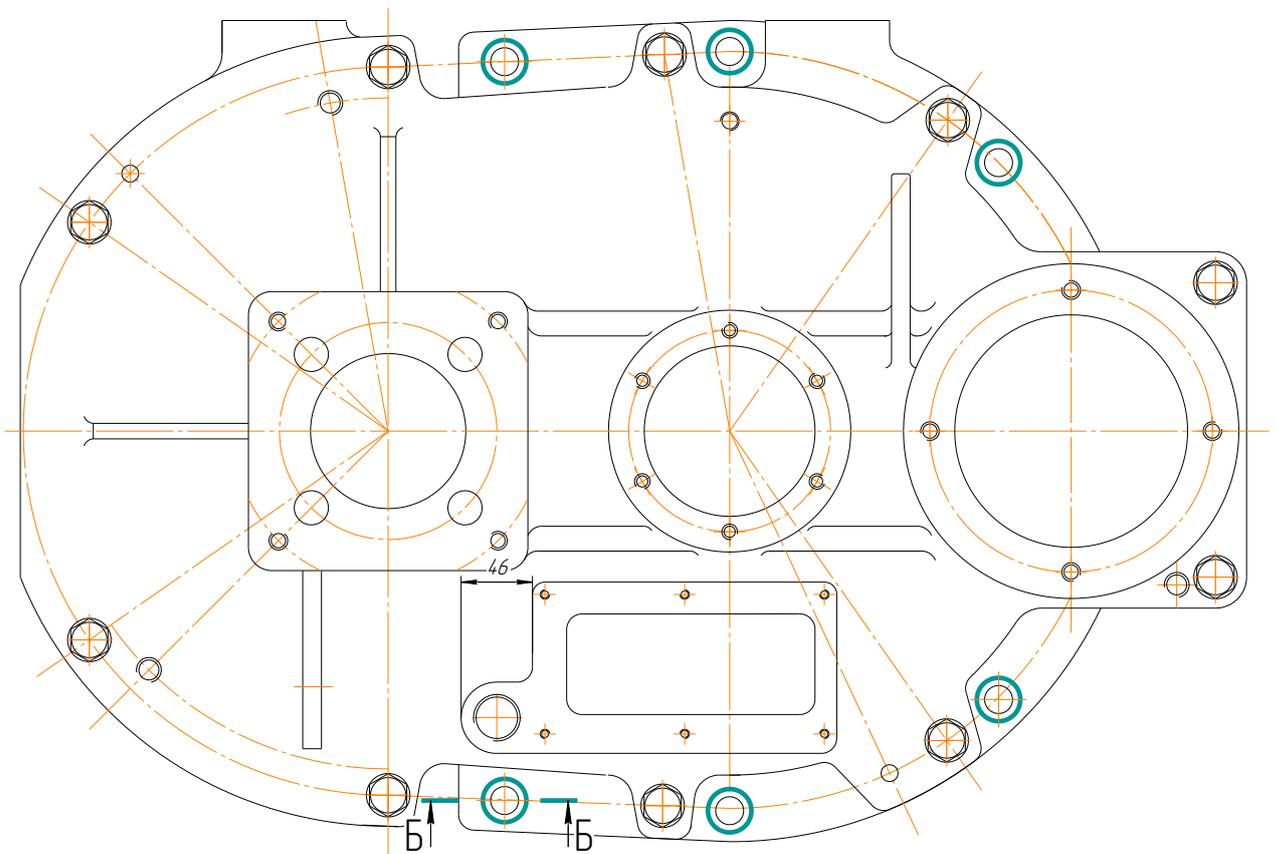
Схема базирования корпуса редуктора в сборе
